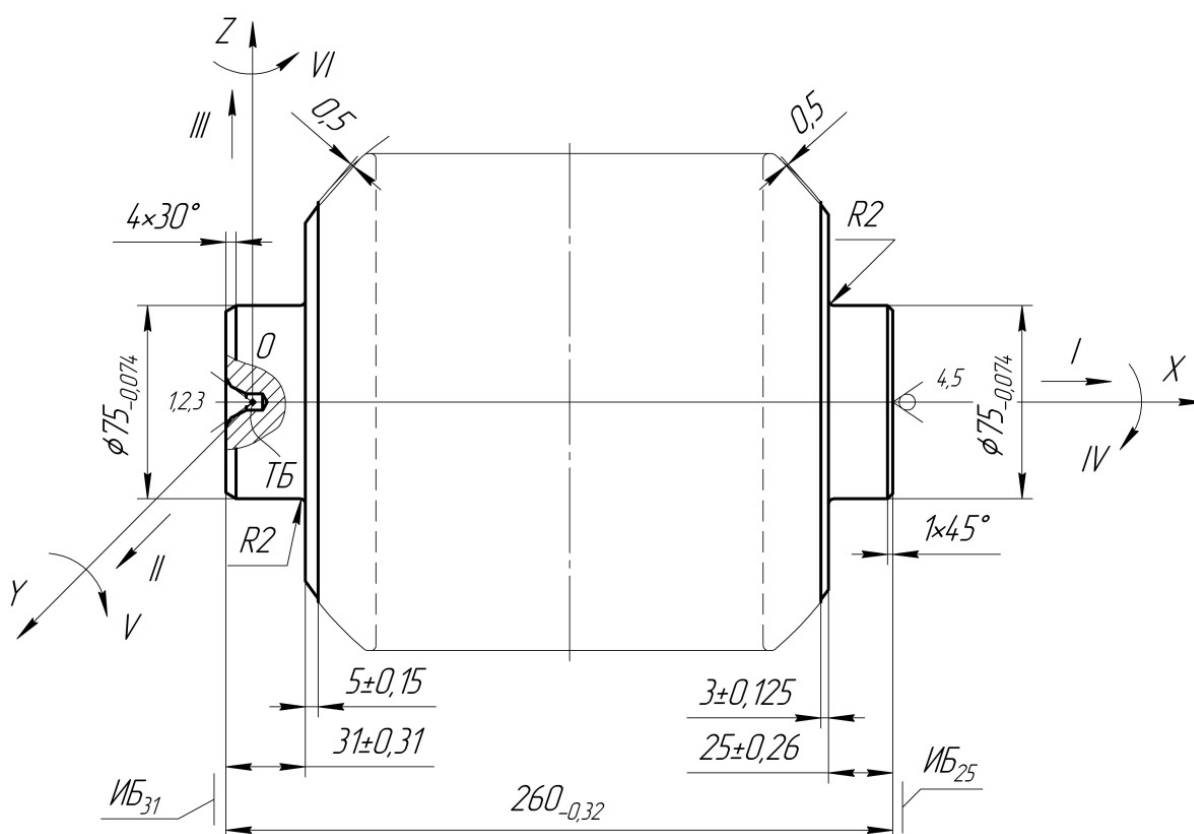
Базування заготовки на операції 035. Схема №1
